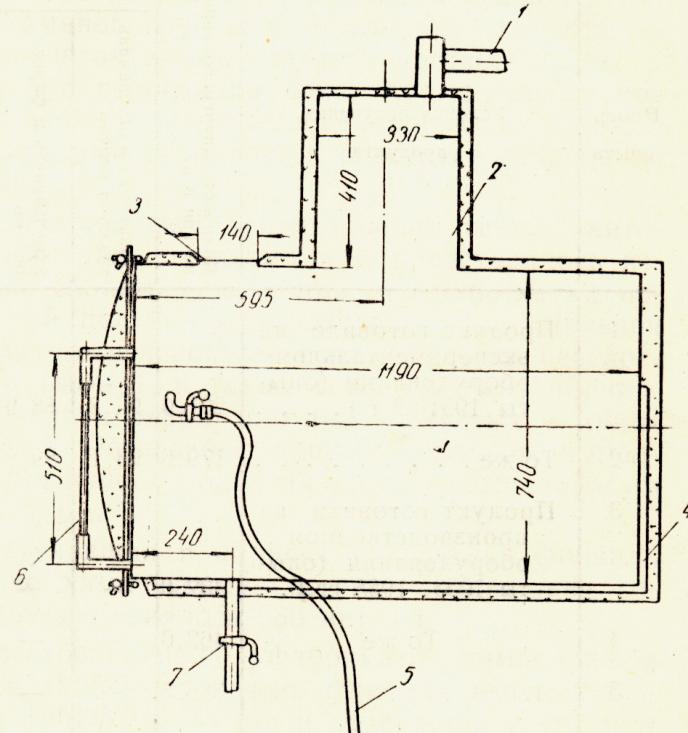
Вакуумный котел для упаривания печеночного сока:
